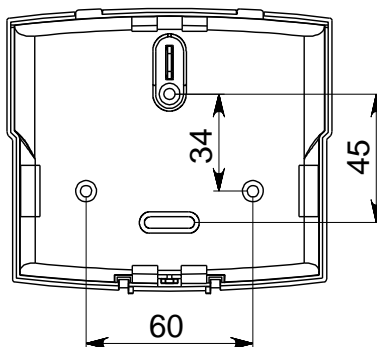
Внешний вид прибора в корпусе с открытой крышкой
